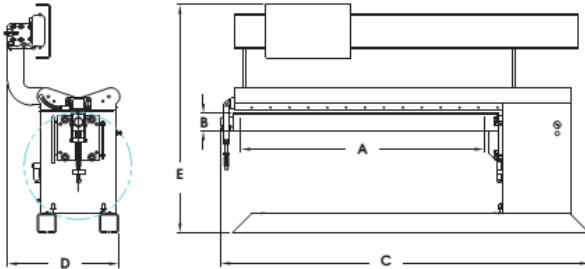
Troca de processo de soldadura nas máquinas (Refª LW) [66]
